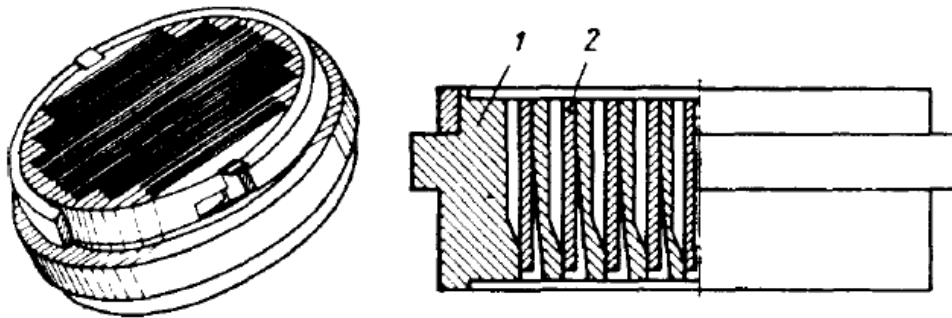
Прямоточний клапан розбірної конструкції: 1 – сідло: 2 – пластина.
